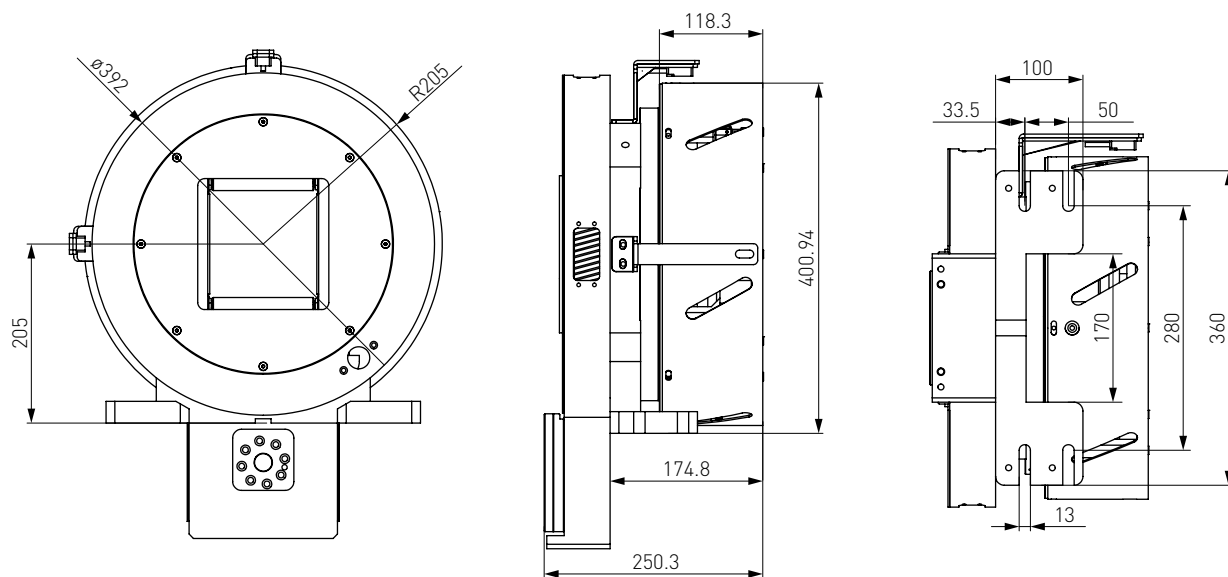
Габаритный чертеж патрона вспомогательного RKQ-120CJYF.
